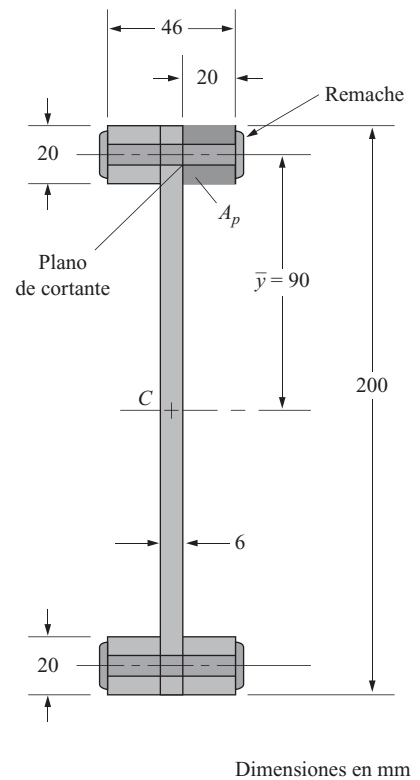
Perfil de viga armado del problema de ejemplo 8-13.
